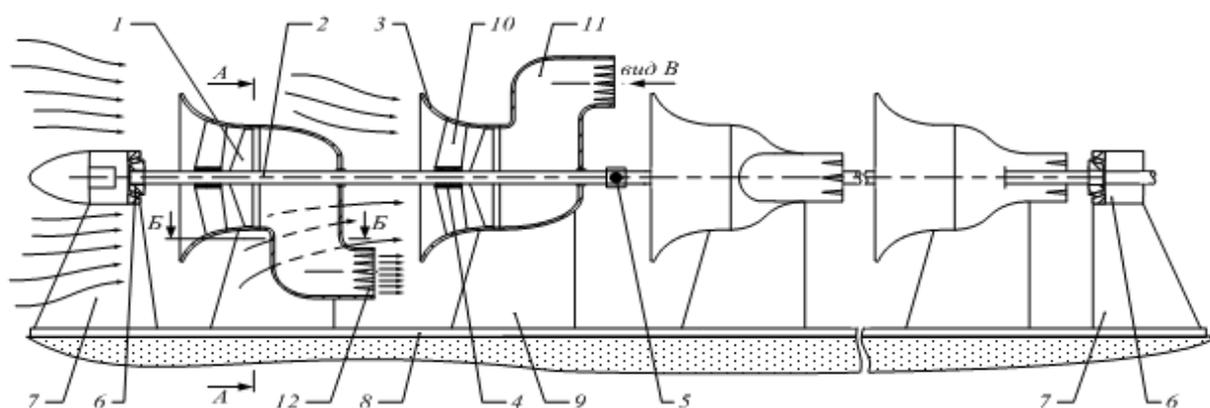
Многоступенчатая гидротурбина (МНГТ): 1 – рабочее колесо; 2 – вал; 3 – кольцевой обтекатель; 4 – подшипник; 5 – шарнирное соединение; 6 – упорный подшипник; 7 – упор; 8 – плита; 9 – ребро; 10 – входной направляющий аппарат; 11 – выходные патрубки; 12 – прорези
